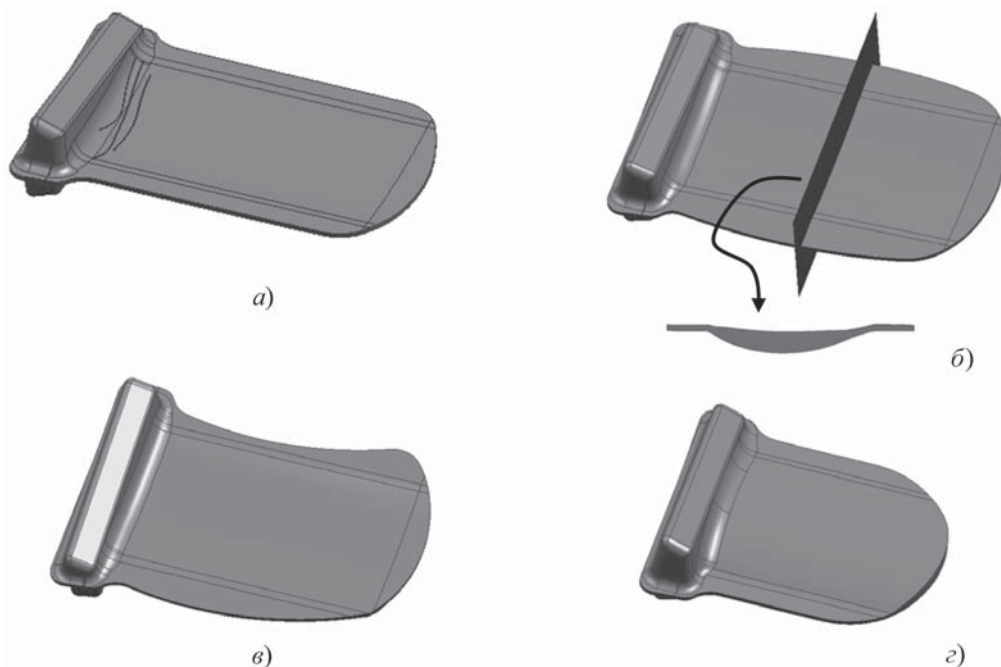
Основные виды дефектов при вальцовке заготовок лопаток газотурбинных двигателей из штучной заготовки:
